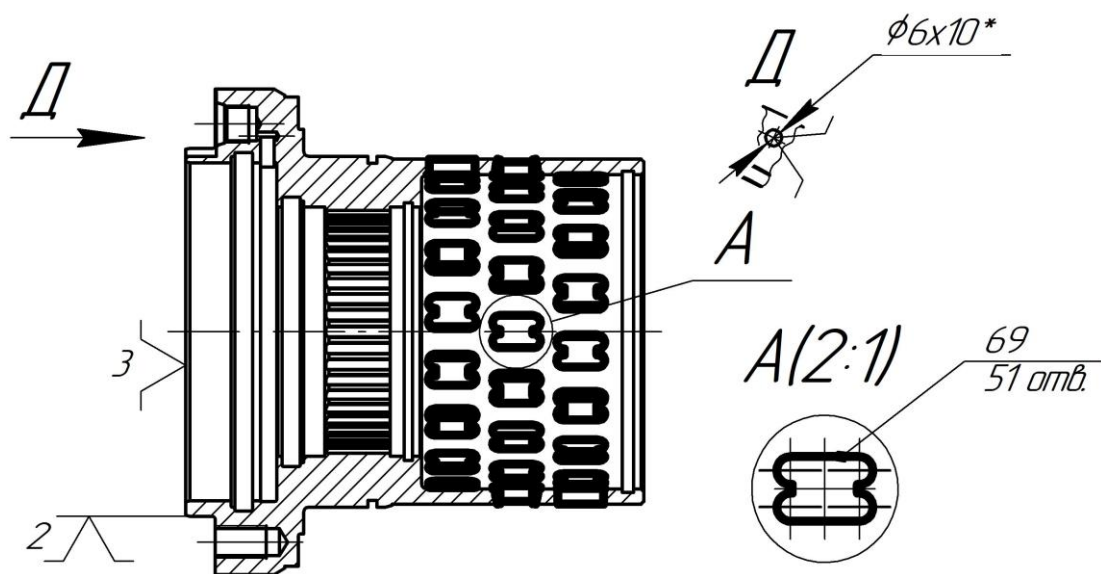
Эскиз фрезерной операции с ЧПУ
